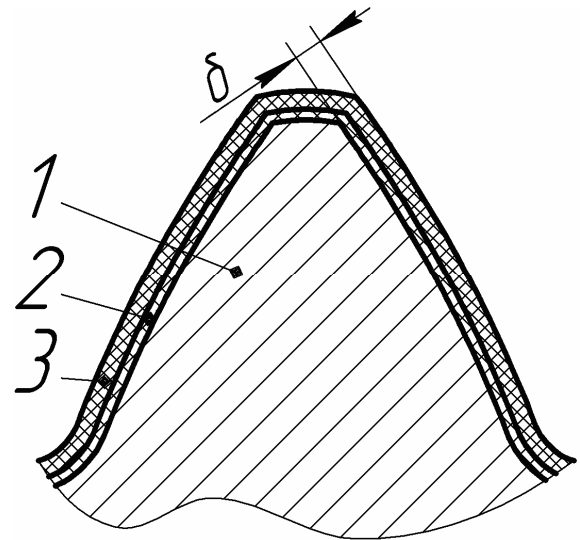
Схема нанесения износоустойчивого покрытия на зуб инструмента: 1 – основа – быстрорежущая сталь; 2 – адгезионный слой; 3 – защитный слой
